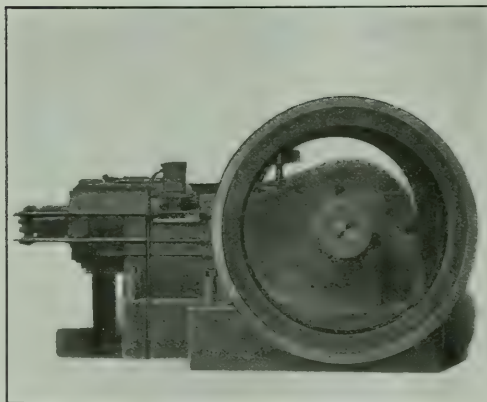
MOTOR HORIZONTAL CONSTRUCCIÓN INGERSOLL-RAND
